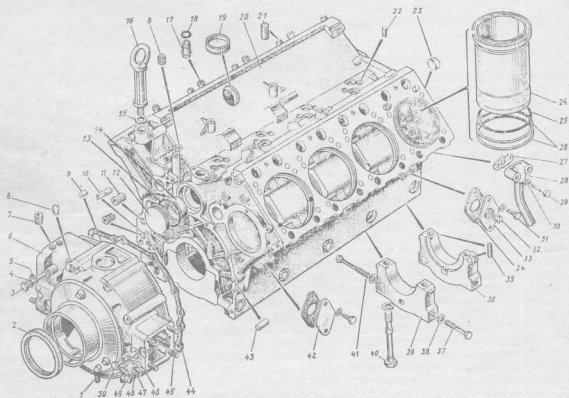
Блок цилиндров с передней крышкой, гильза цилиндра:
